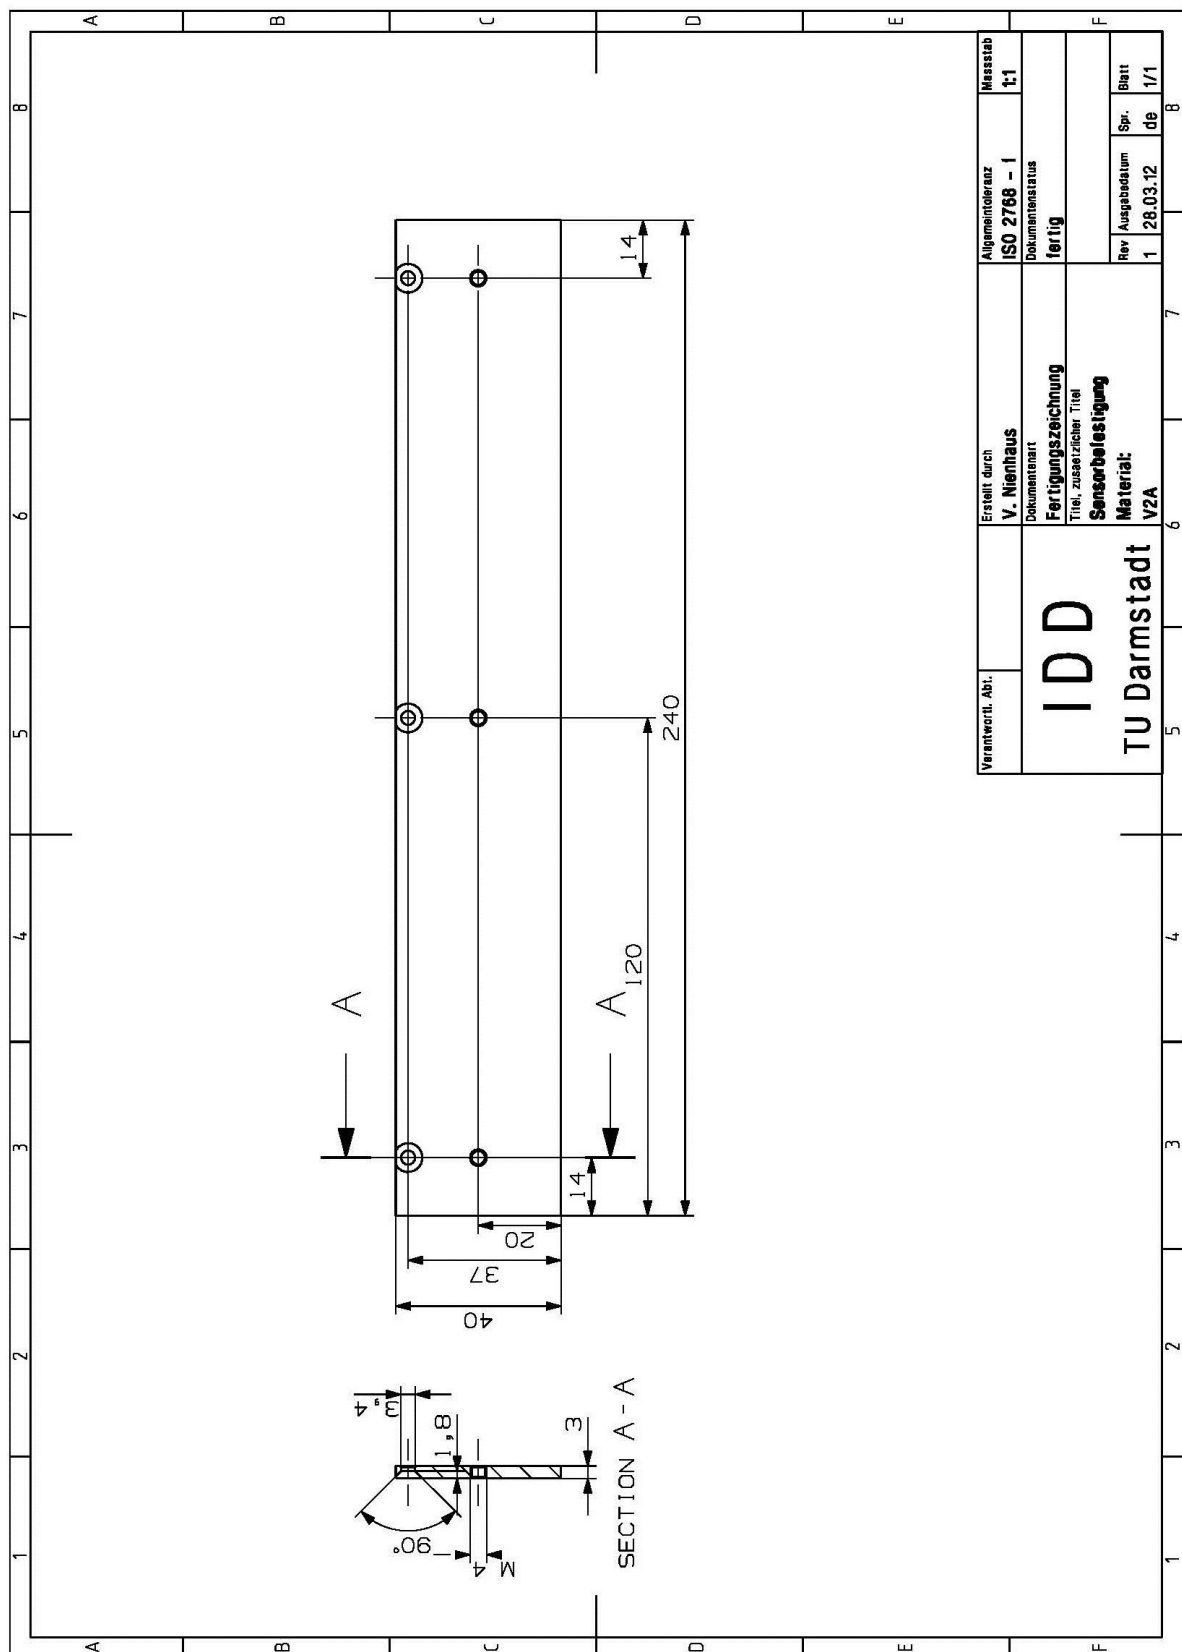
Zeichnung der Halterung für die Thermoelemente beim Temperaturmessaufbau an der Prägefoliendruckmaschine GEBA 6 der Firma Baier. Teil 1: Befestigungsplatte.
